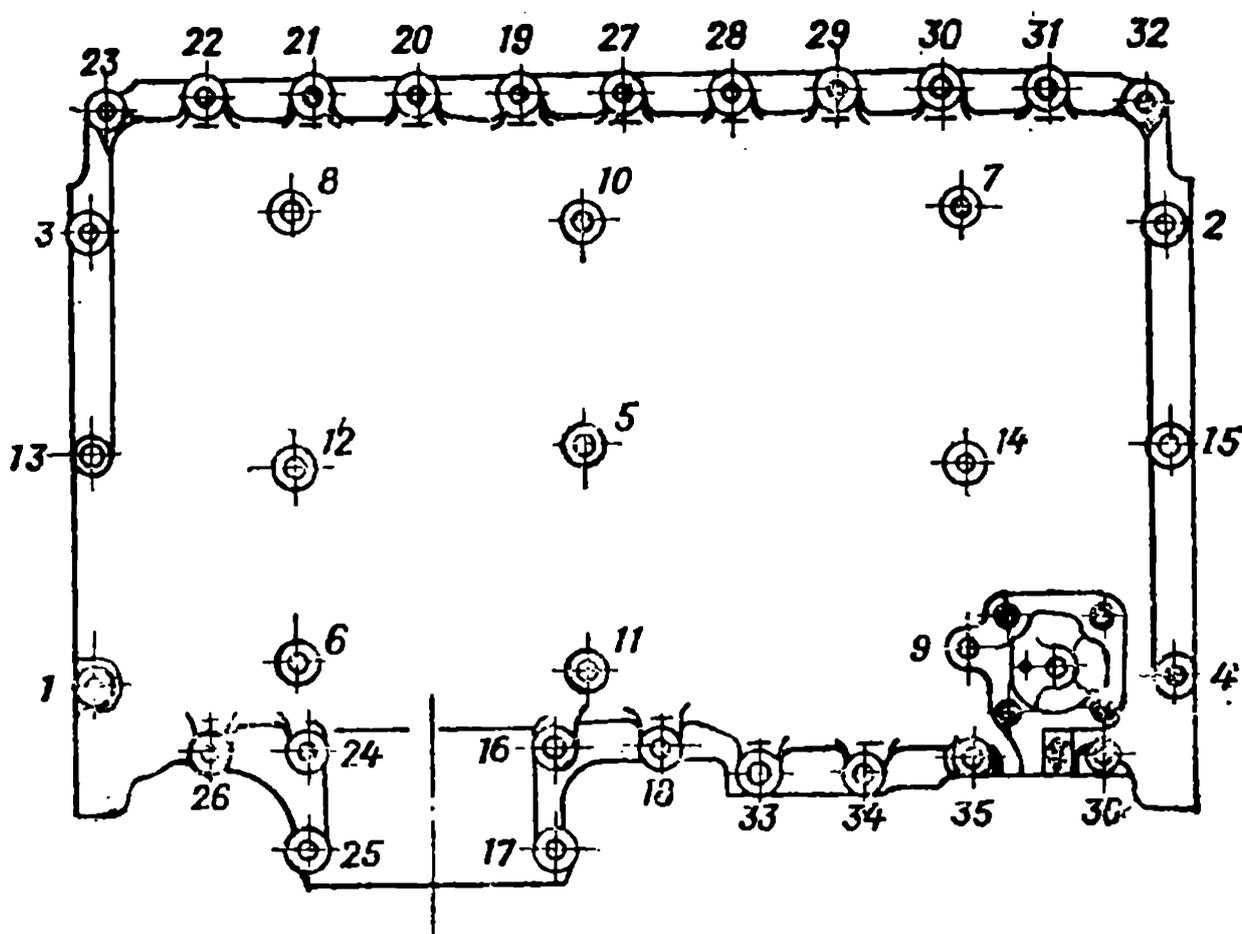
Порядок затяжки гаек крепления крышки главной передачи
